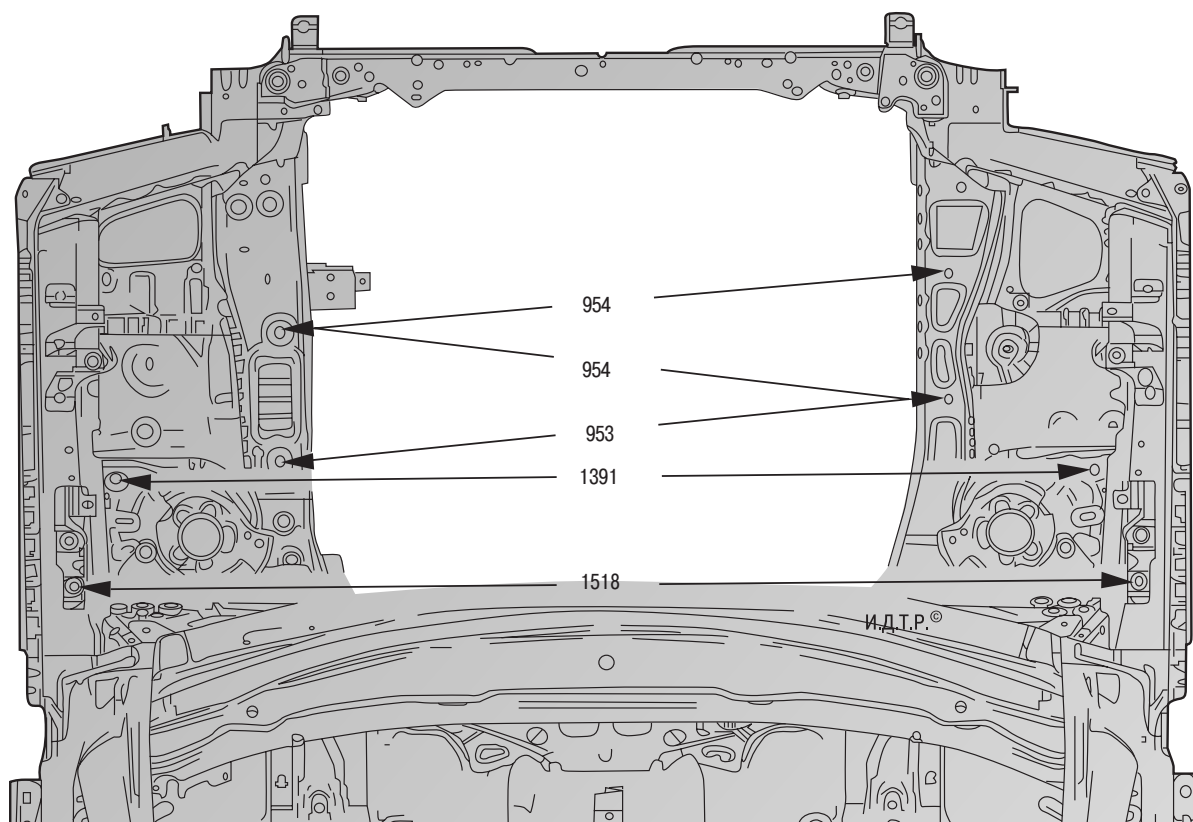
Контрольные размеры моторного отсека (вид сверху)
